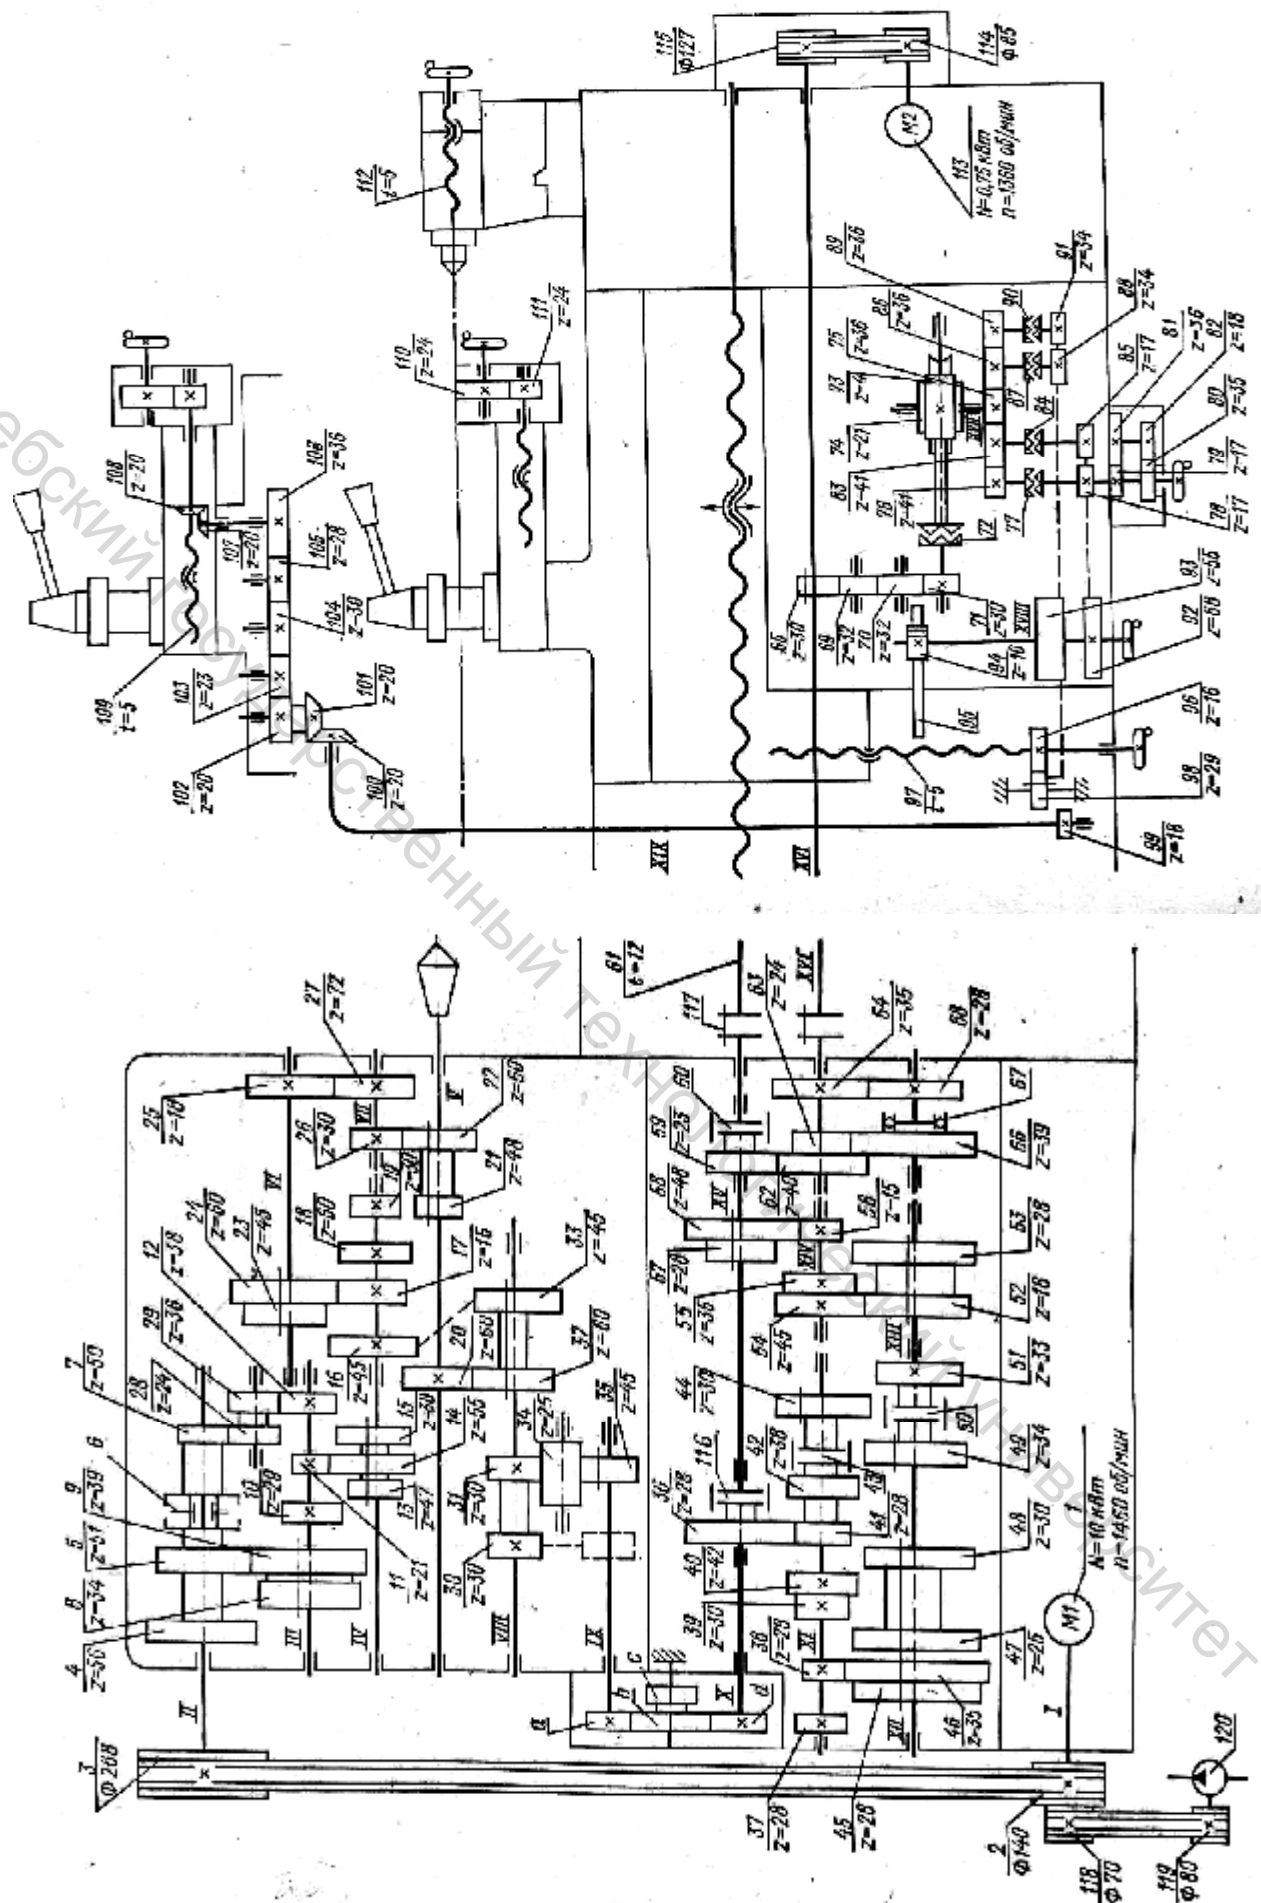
Кинематическая схема токарного станка мод. 16K20.
